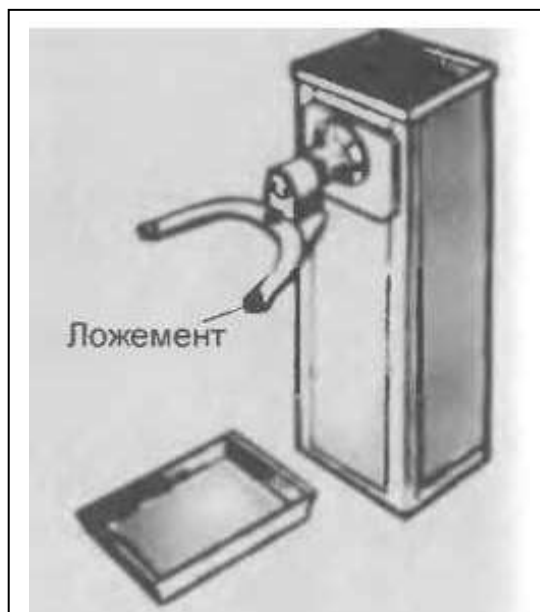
Стенд для разборки и сборки редукторов мостов автомобиля
